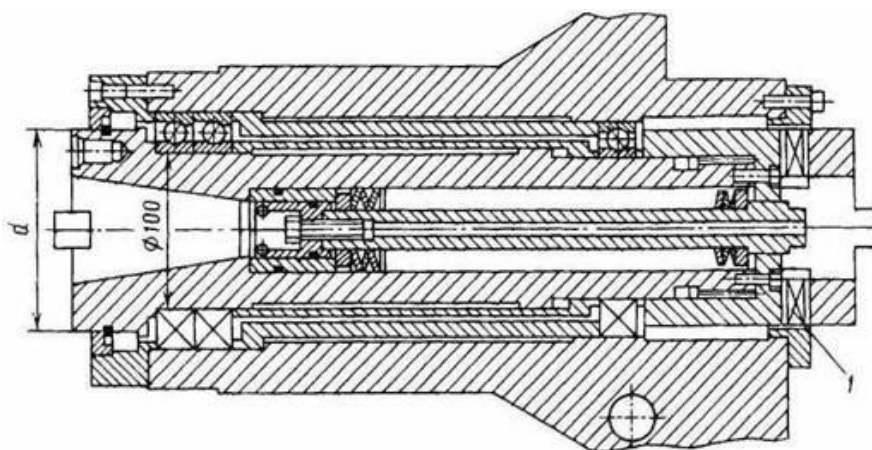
Шпиндельный узел сверлильно-фрезерно-расточного станка
